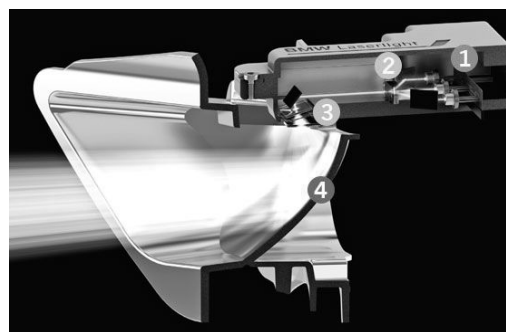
Конструкция лазерной фары серийного гибридного автомобиля BMW i8 [3]: 1 – лазерные диоды; 2 – оптическая система; 3 – пластина с люминофором; 4 – металлический рефлектор
